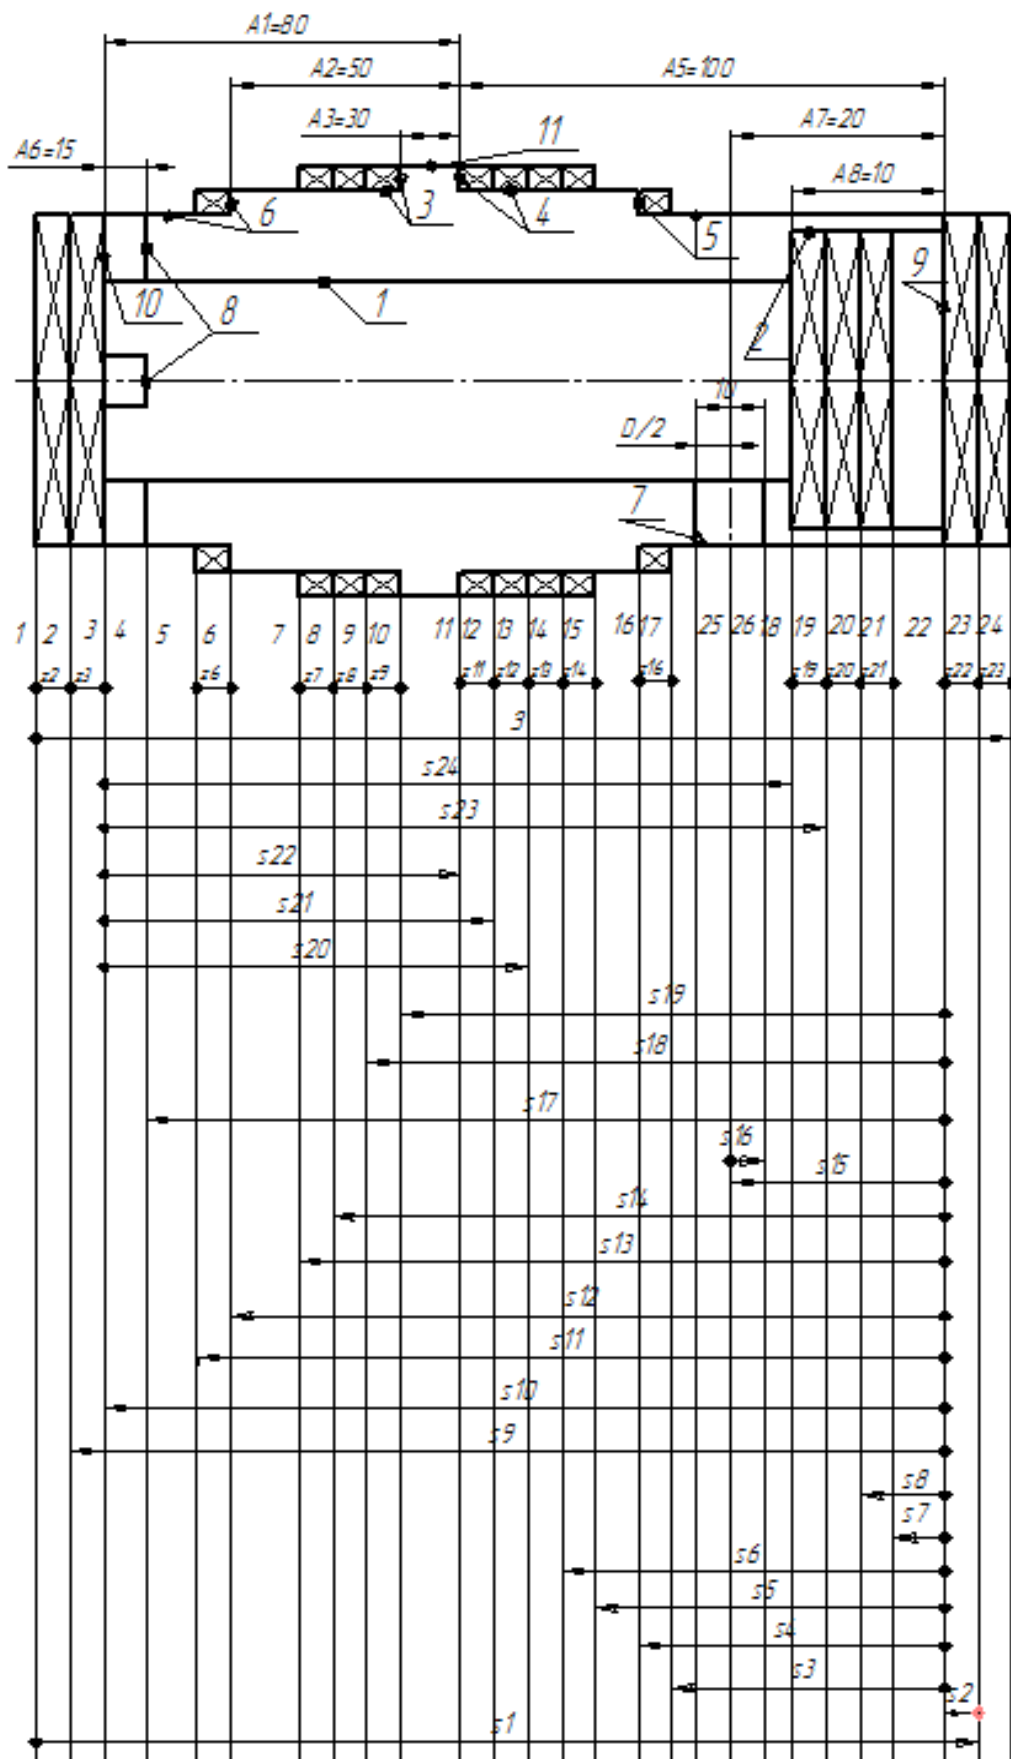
Размерная схема первого маршрута изготовления детали
